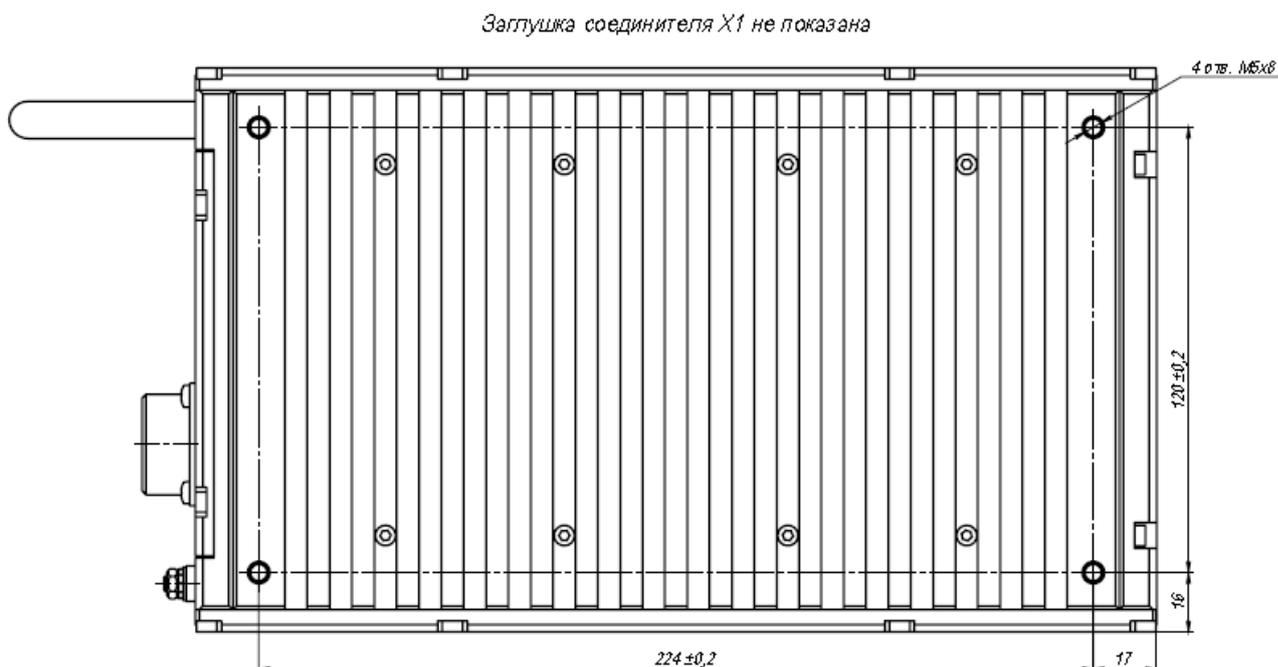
2 - Расположение монтажных отверстий ИСС300
